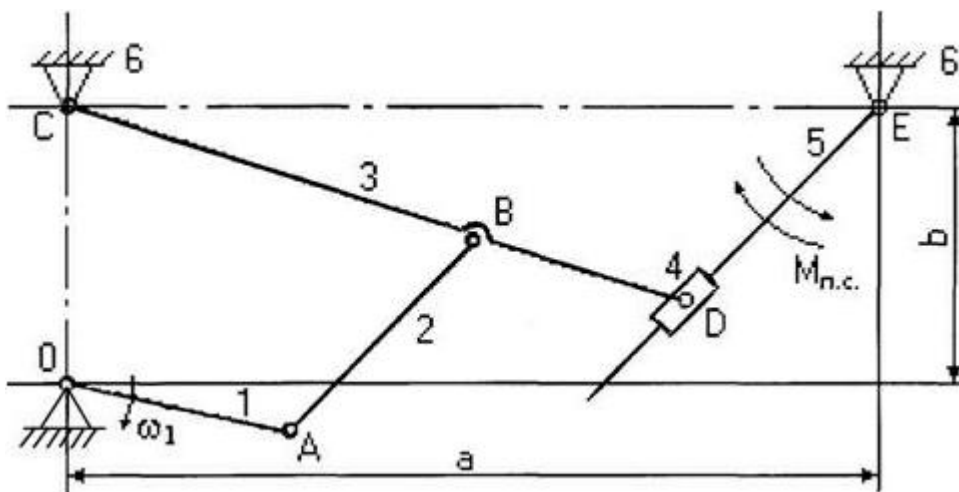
Кинематическая схема плоского рычажного механизма
